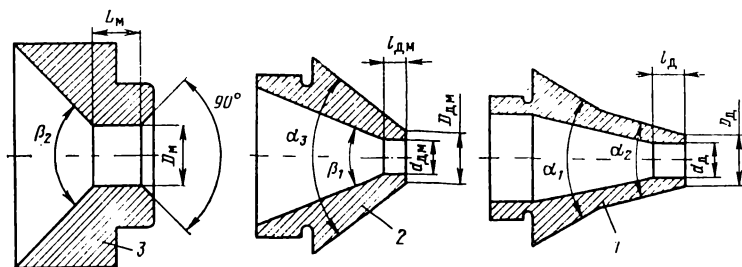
Формующий инструмент для двухслойного наложения резиновых герметизирующих заполнений и оболочки.
